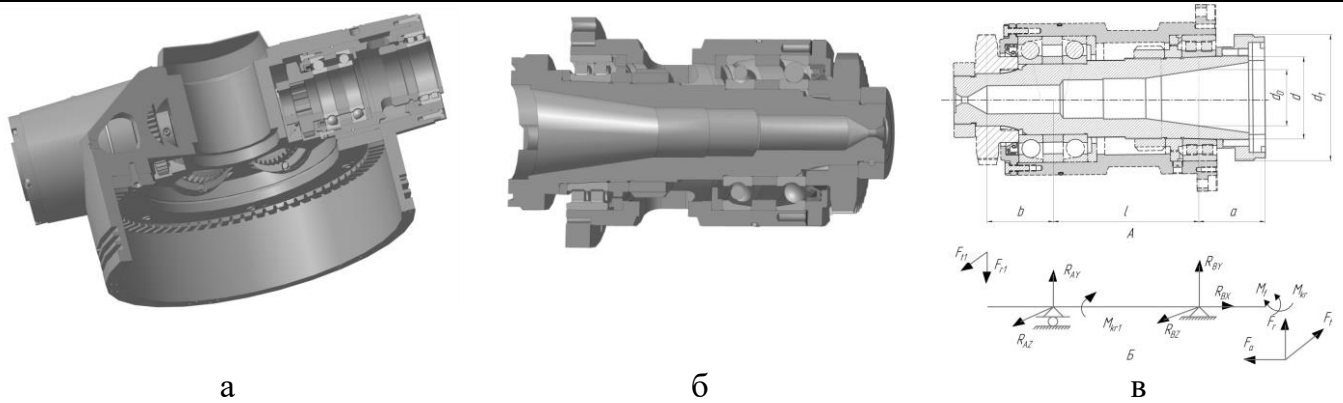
Револьверна головка: а – складення; б – шпиндельний вузол; в – креслення
